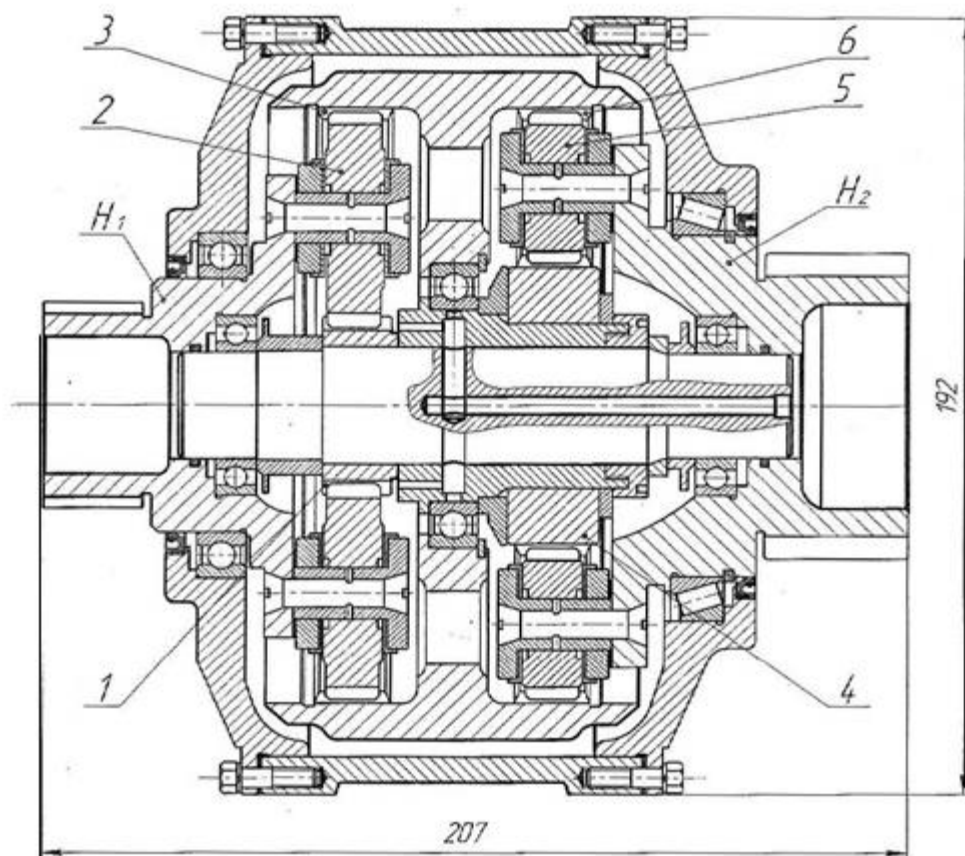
Сборочный чертеж предполагаемого вариатора
